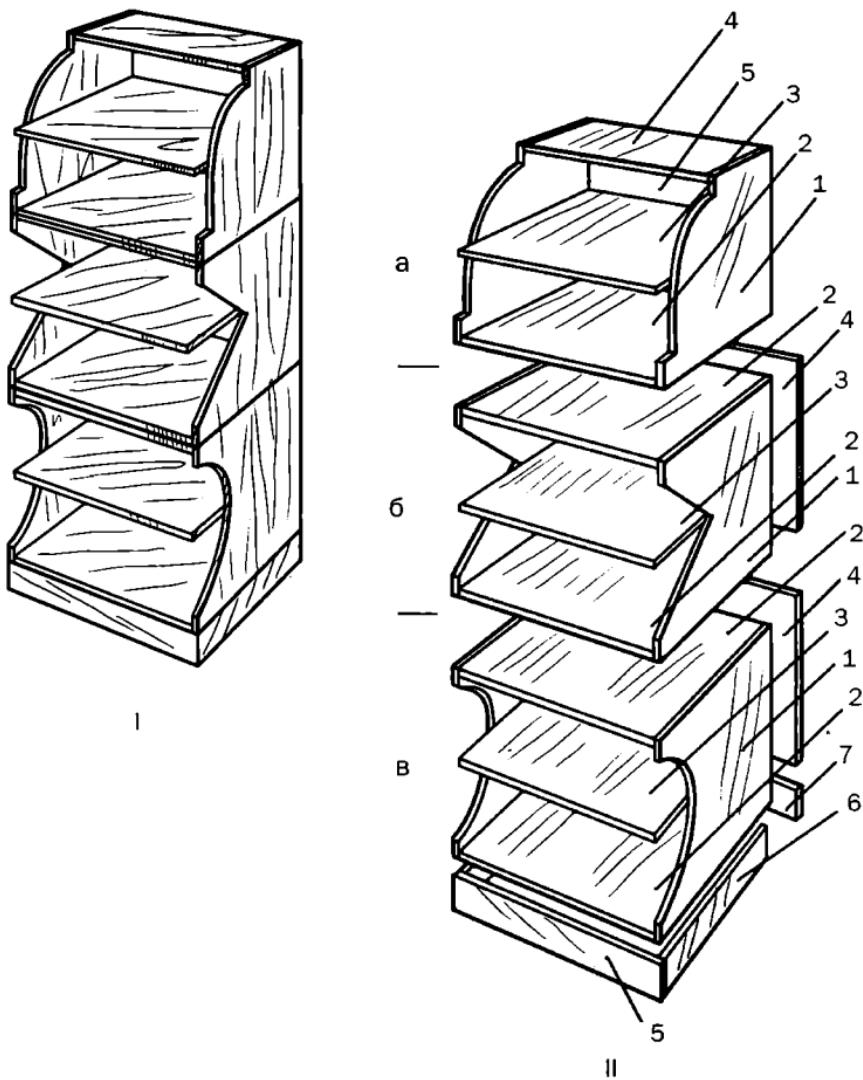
Модульный стеллаж: I — общий вид; II — схема сборки:
